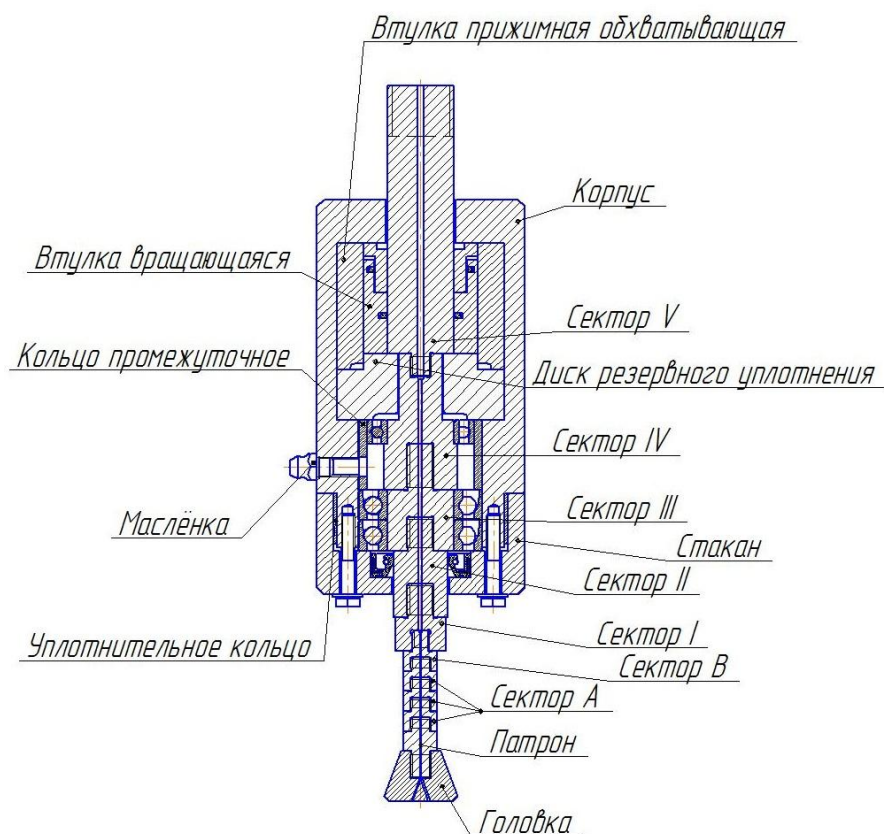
Сопло для обработки поверхностей в разрезе
